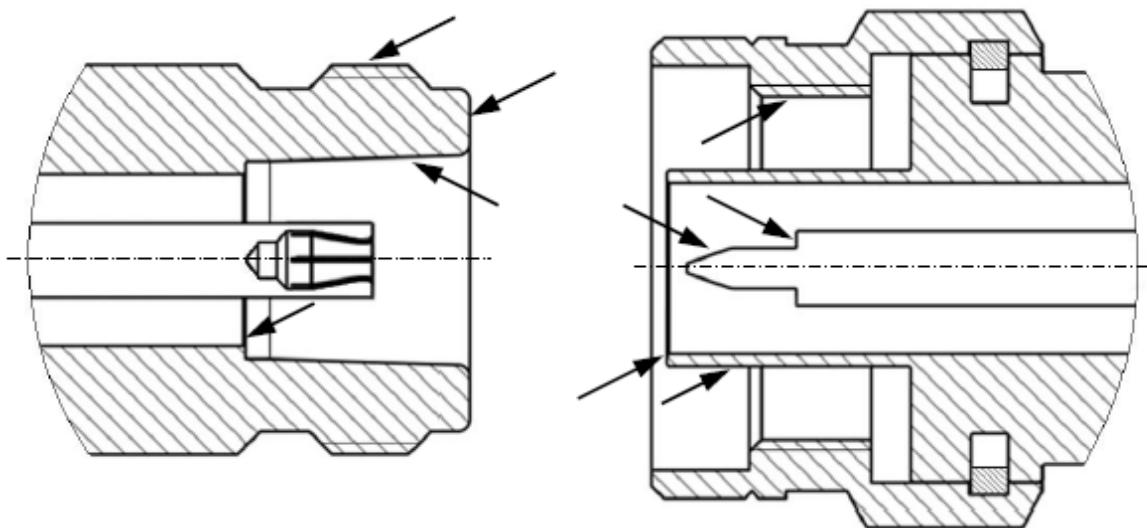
Соединители тип N и III (розетка и вилка)
